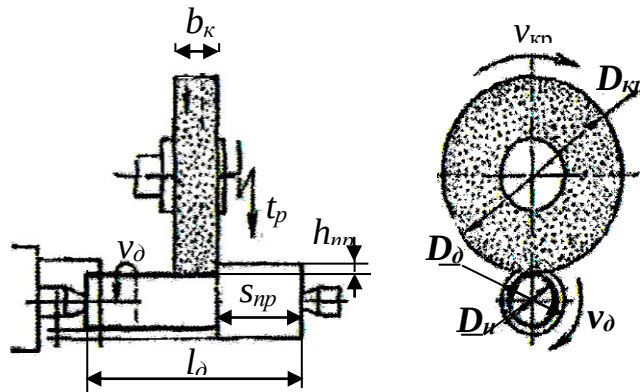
Схема обработки шлифовальным кругом деталей класса "валы":
